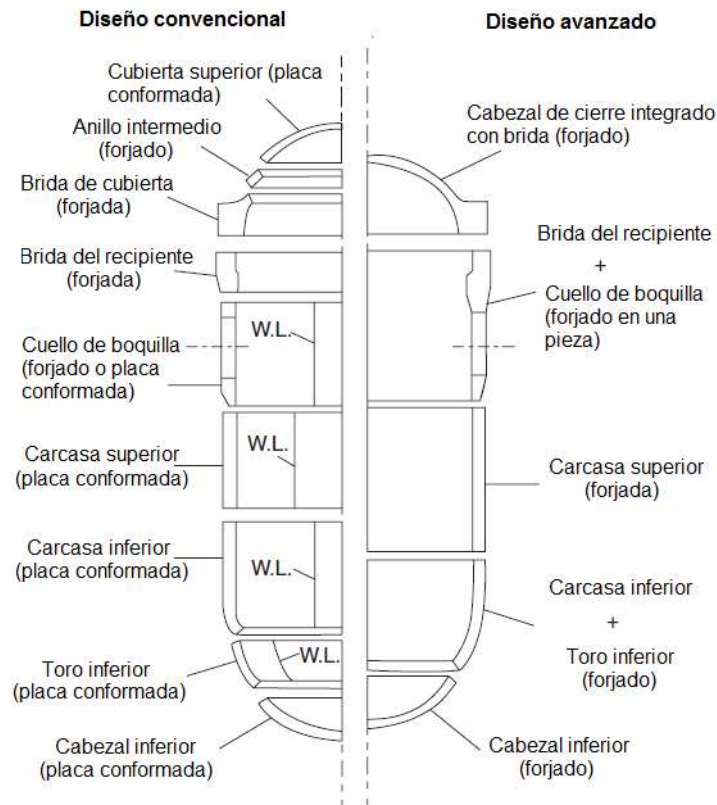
Diseños convencional y avanzado de un RPR [19]. W.L.: línea de soldadura.
